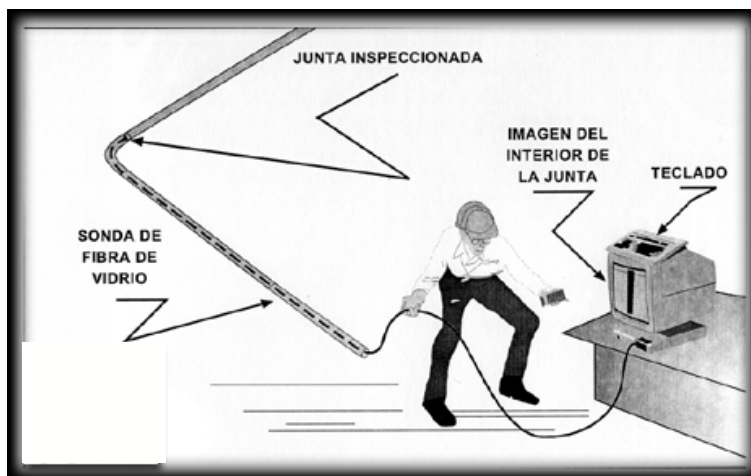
Inspección de Soldaduras en Tubería por Medio de Boroscopia.
